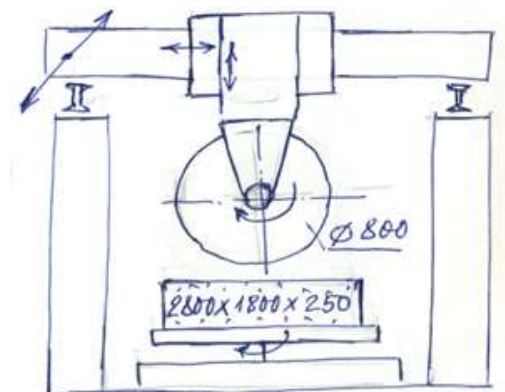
Мостовий фрезерно-обкантовувальний верстат моделі СМР-015.
